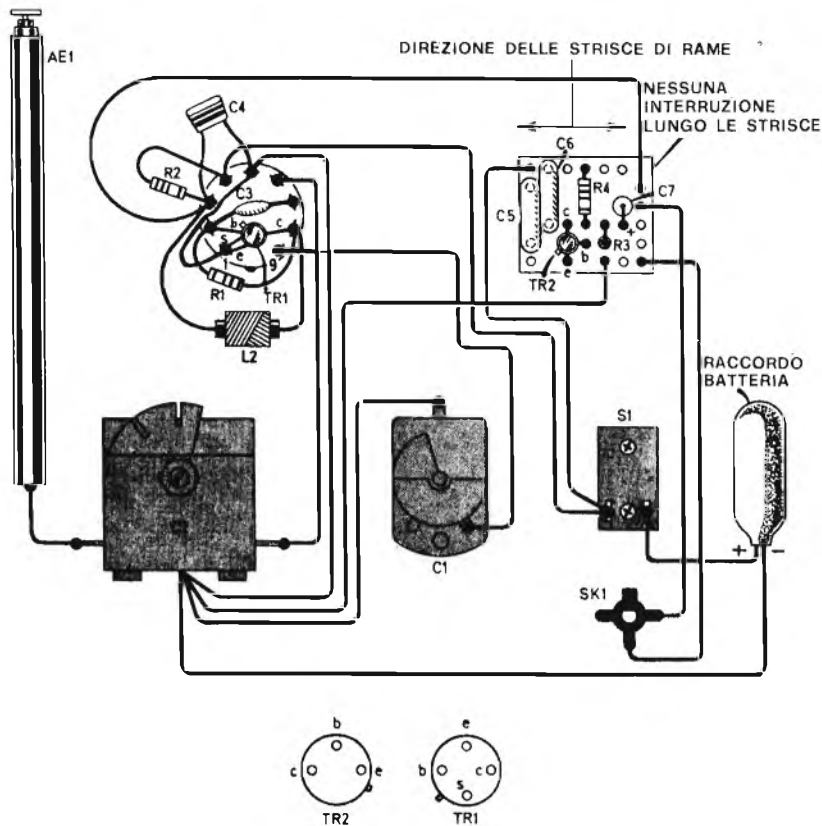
Piano di cablaggio dell'intero ricevitore: si notino i componenti che devono essere ancorati direttamente ai terminali della bobina ed i collegamenti che uniscono la piastrina di supporto alla parte restante del circuito. Al di sotto di questo disegno sono riportati i collegamenti allo zoccolo di TR1 e TR2, visti dal di sotto.
